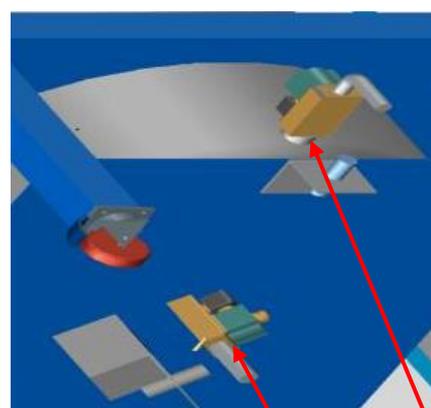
Diseño de los componentes mecánicos dentro del tanque
